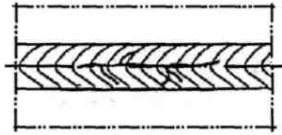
11. Разветвленная трещина сварного соединения
